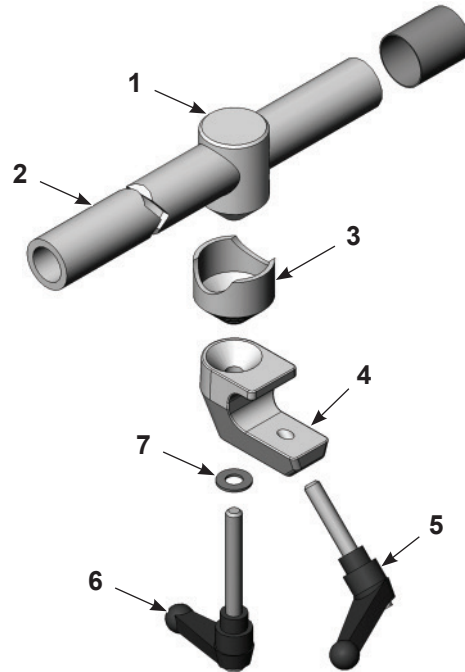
Barre pour pistolets de pulvérisation à fixation sur barre
